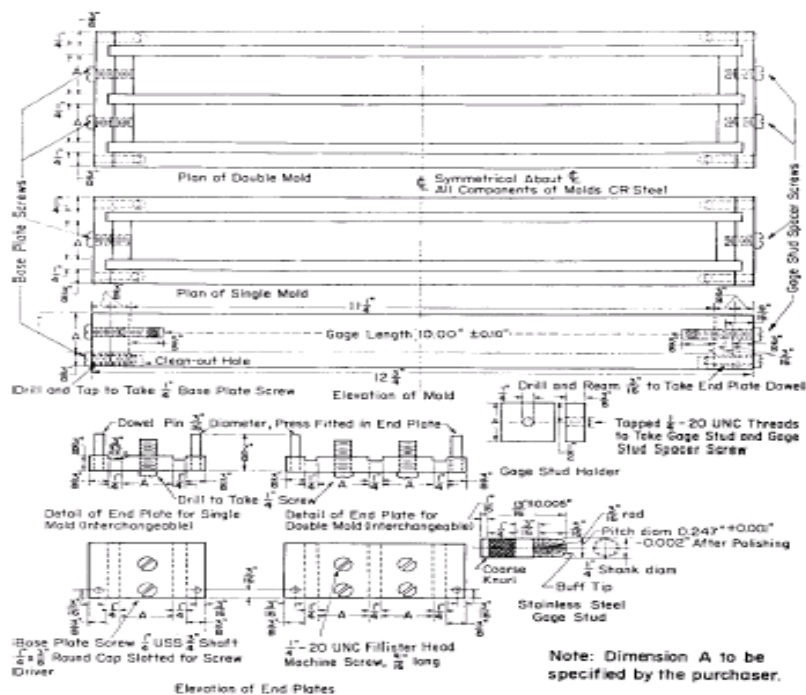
moldes para especimenes (en unidades inglesas)
